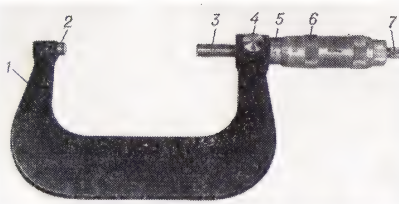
Гладкий микрометр МГ с пределами измерения 75—100 мм: 1 — скоба; 2 — пятка; 3 — микрометрический винт; 4 — стопор; 5 — стебель; 6 — барабан; 7 — трещотка.
